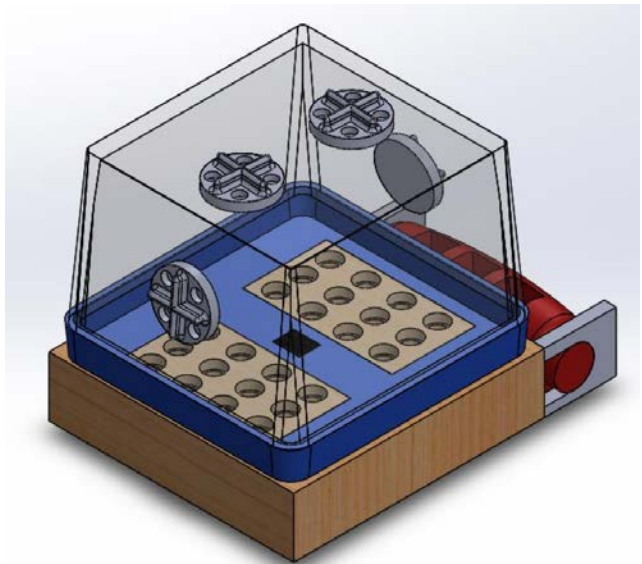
Diseño del germinador utilizando SolidWorks™.
